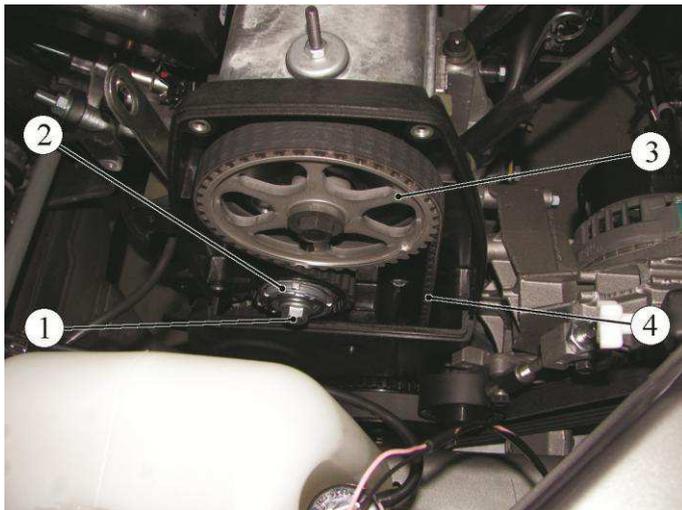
Снятие ремня привода ГРМ на двигателях 11186 и 21116:
